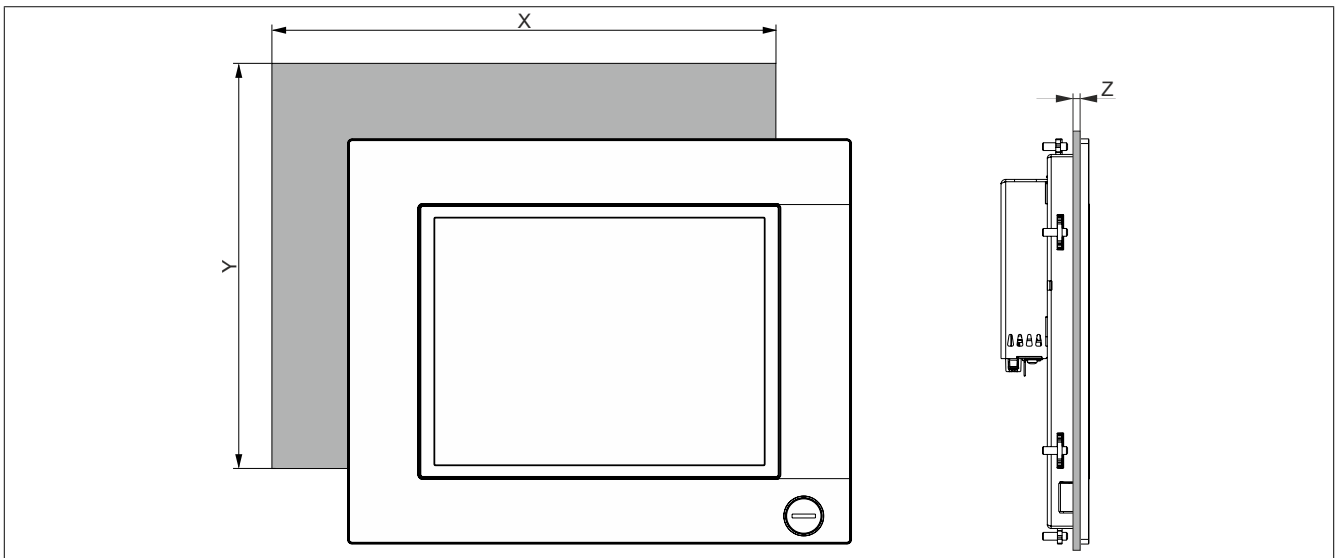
Einbauzeichnung - Panel PC 2100 mit AP1000 Panels mit Halteklammern (Beispielabbildung)
